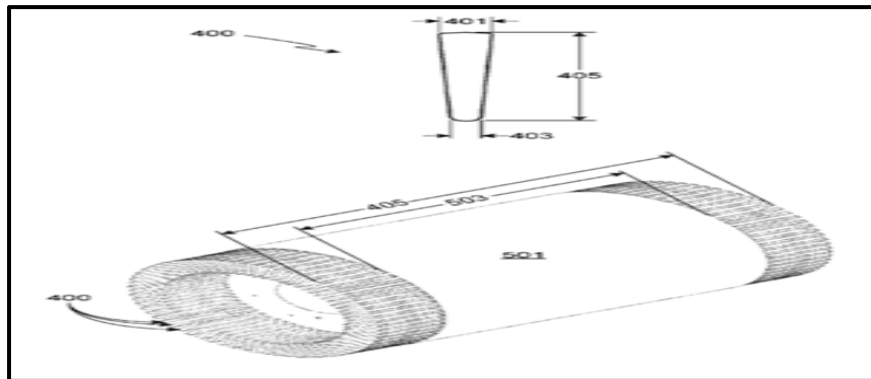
Sección transversal de una barra de rotor y un conjunto de discos laminados que conforman el rotor (Lyons, D.; Tesla Motors, Inc.; Straubel, J., 2013).
